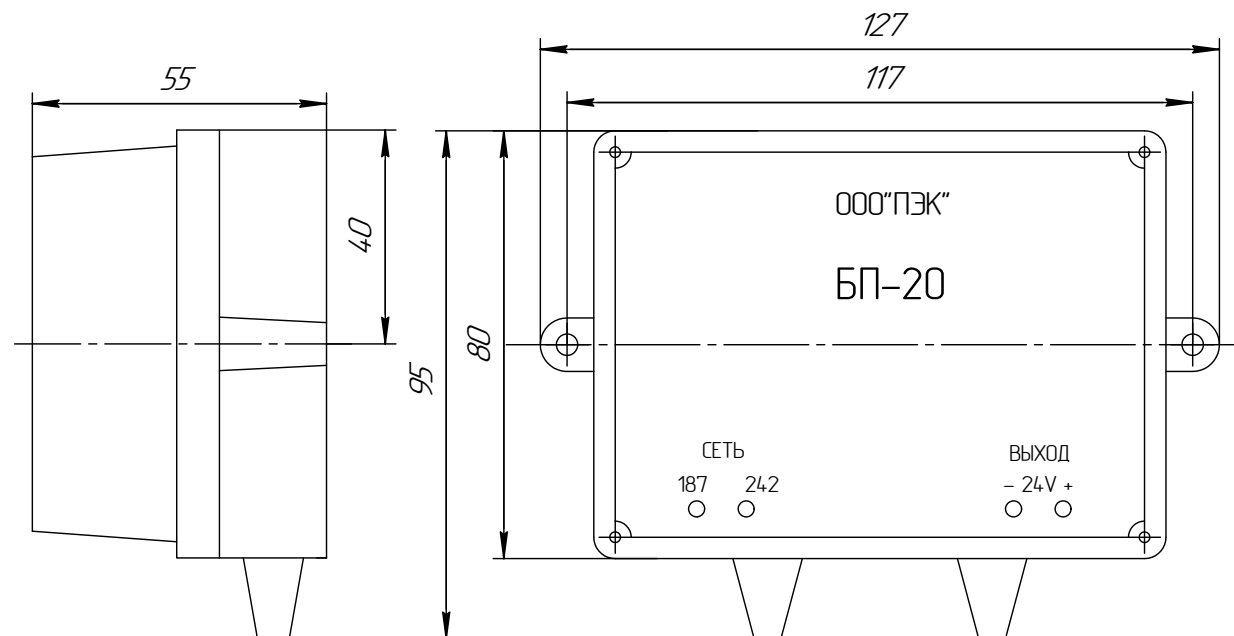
Габаритные размеры блока питания БП-20
